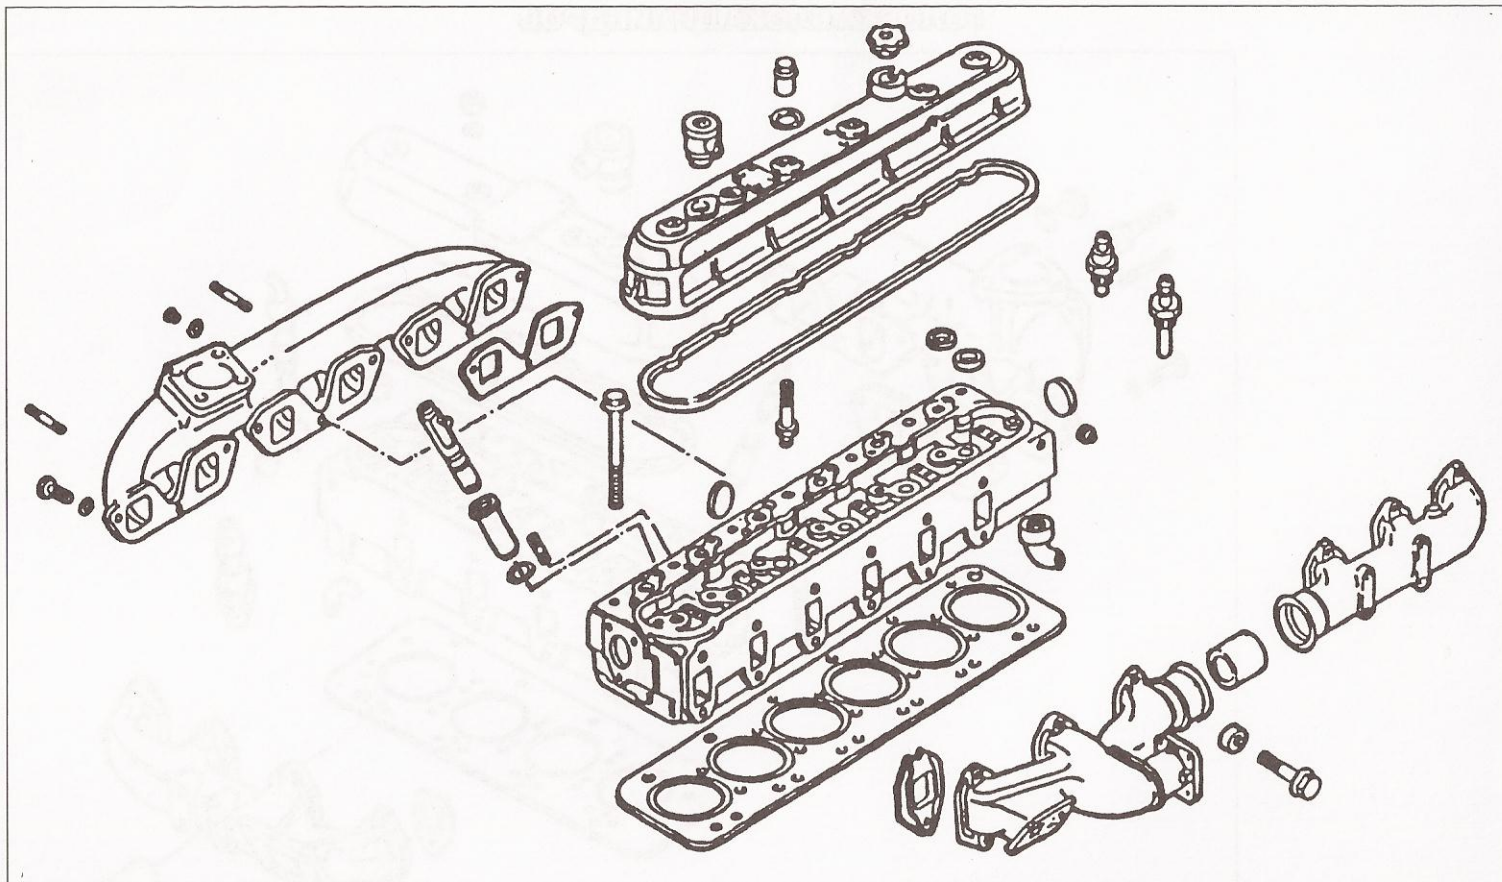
Головка блока цилиндров (6-цилиндровый двигатель)
